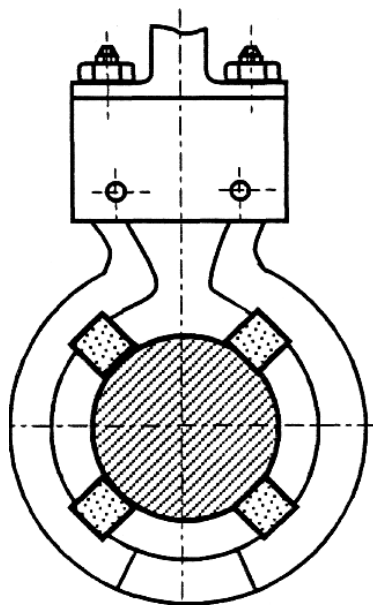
Схема хонингования цилиндрической поверхности.
